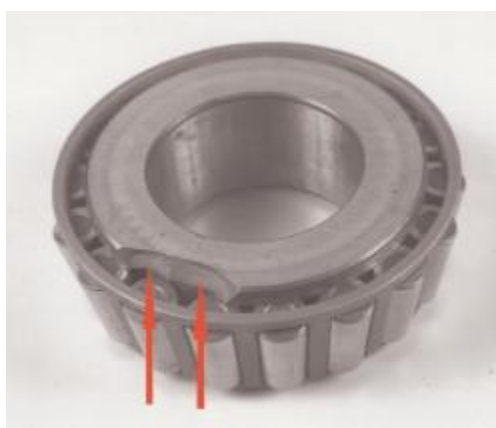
由装配过程中冲击载荷引起的圆锥滚子轴承内圈挡边过载断裂
